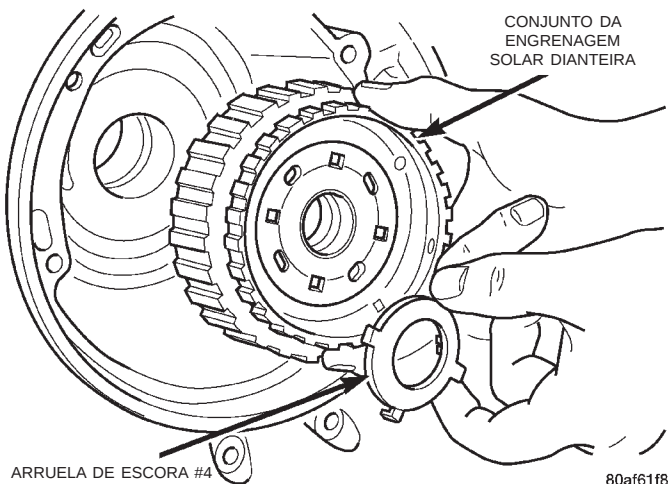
Instalação do Conjunto da Engrenagem Solar Dianteira
